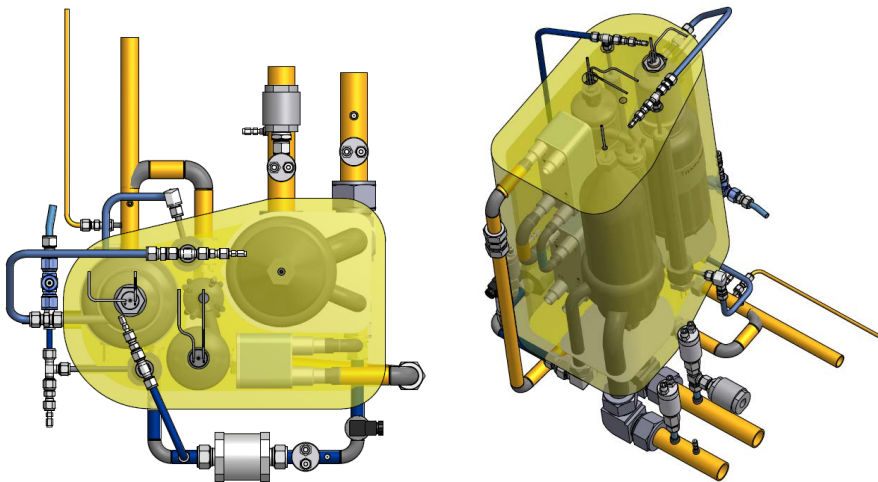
2. Entwurf für das Package Fuel Processing-System, links Draufsicht, rechts: Seitenansicht der Isometrie
